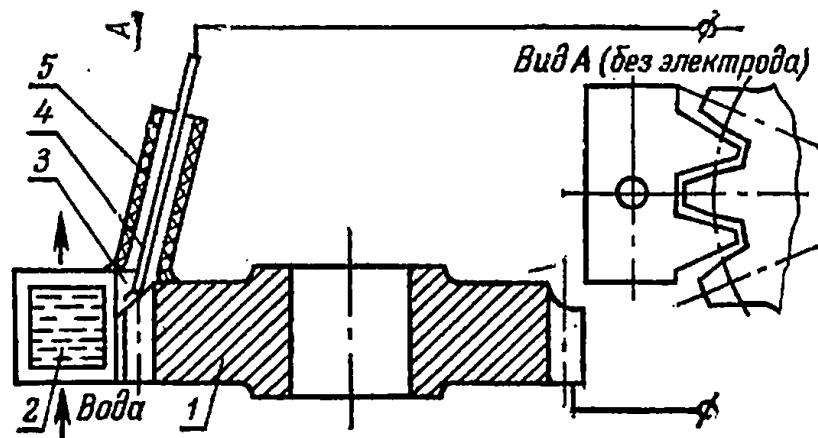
Схема наплавки изношенных торцевых поверхностей зубьев шестерен:
